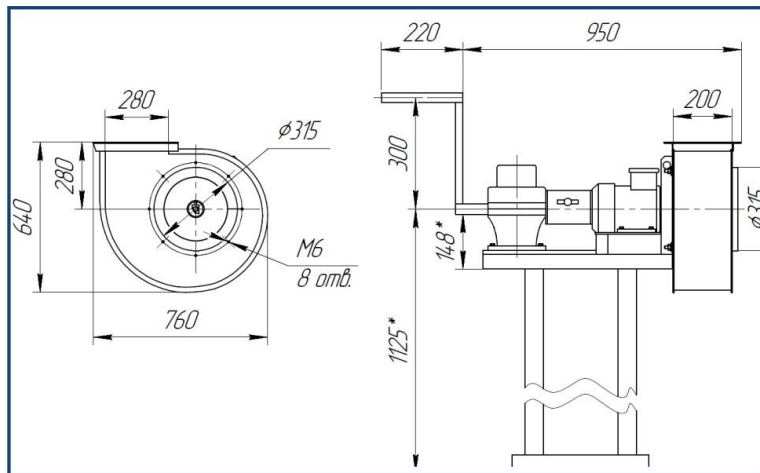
Габаритні та приєднувальні розміри вентилятора ЕРВ-4
